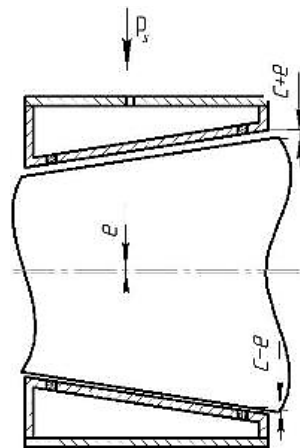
Газостатический конический подшипник с пористыми вставками
